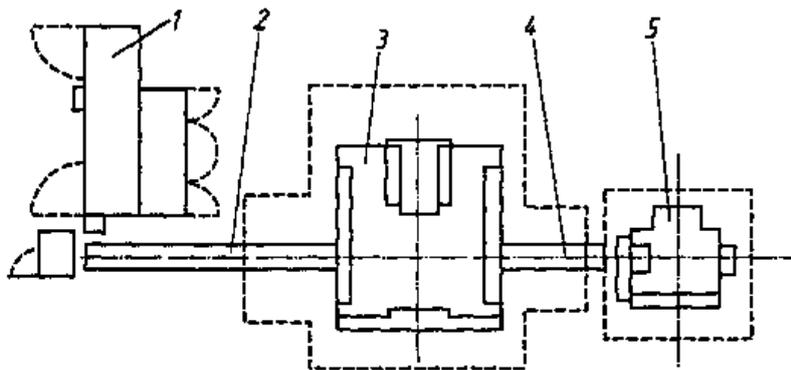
Схема поточной линии штамповки заготовок шестерен на механическом ковочном прессе: 1 – ковочно-индукционный нагреватель; 2 – цепной транспортер; 3 – кривошипный ковочно-штамповочный пресс усилием 1500 тс.; 4 – пластинчатый транспортер; 5 – обрезающий пресс усилием 160 тс
